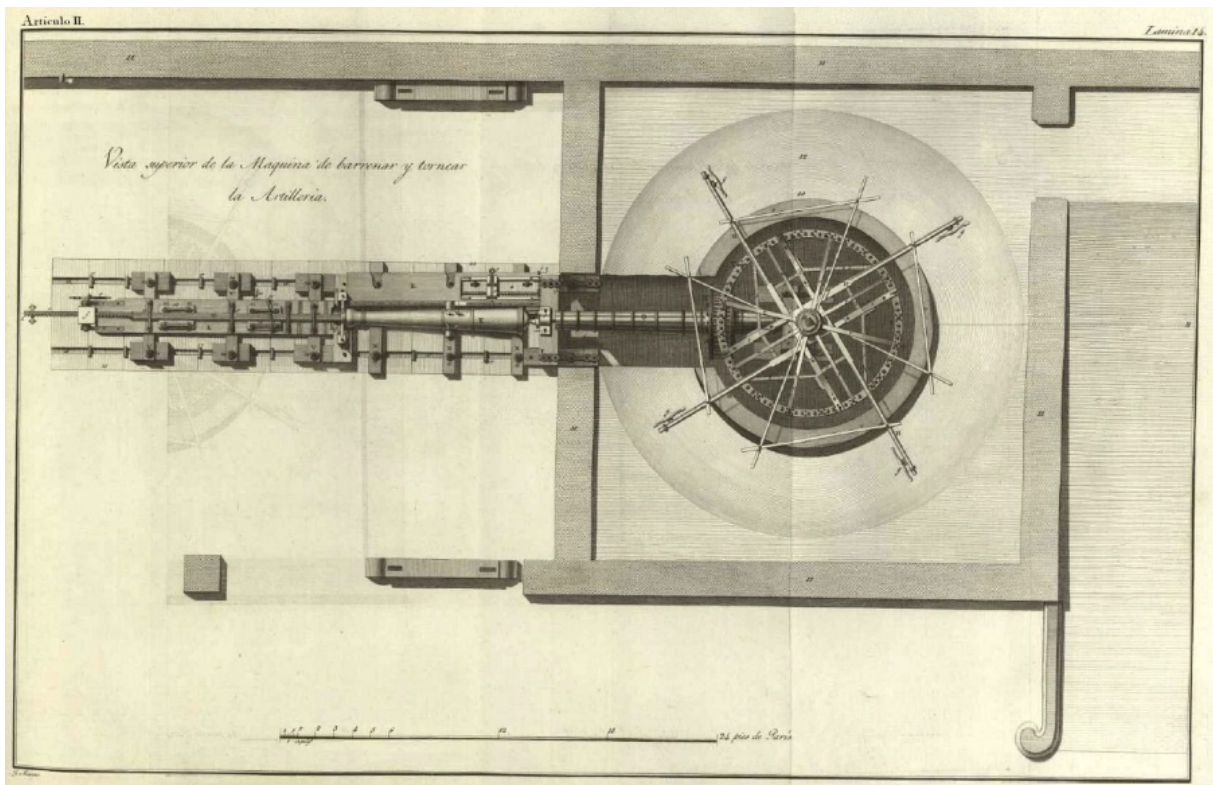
Plano de planta de la máquina para barrenar y torner las piezas de artillería [3].
